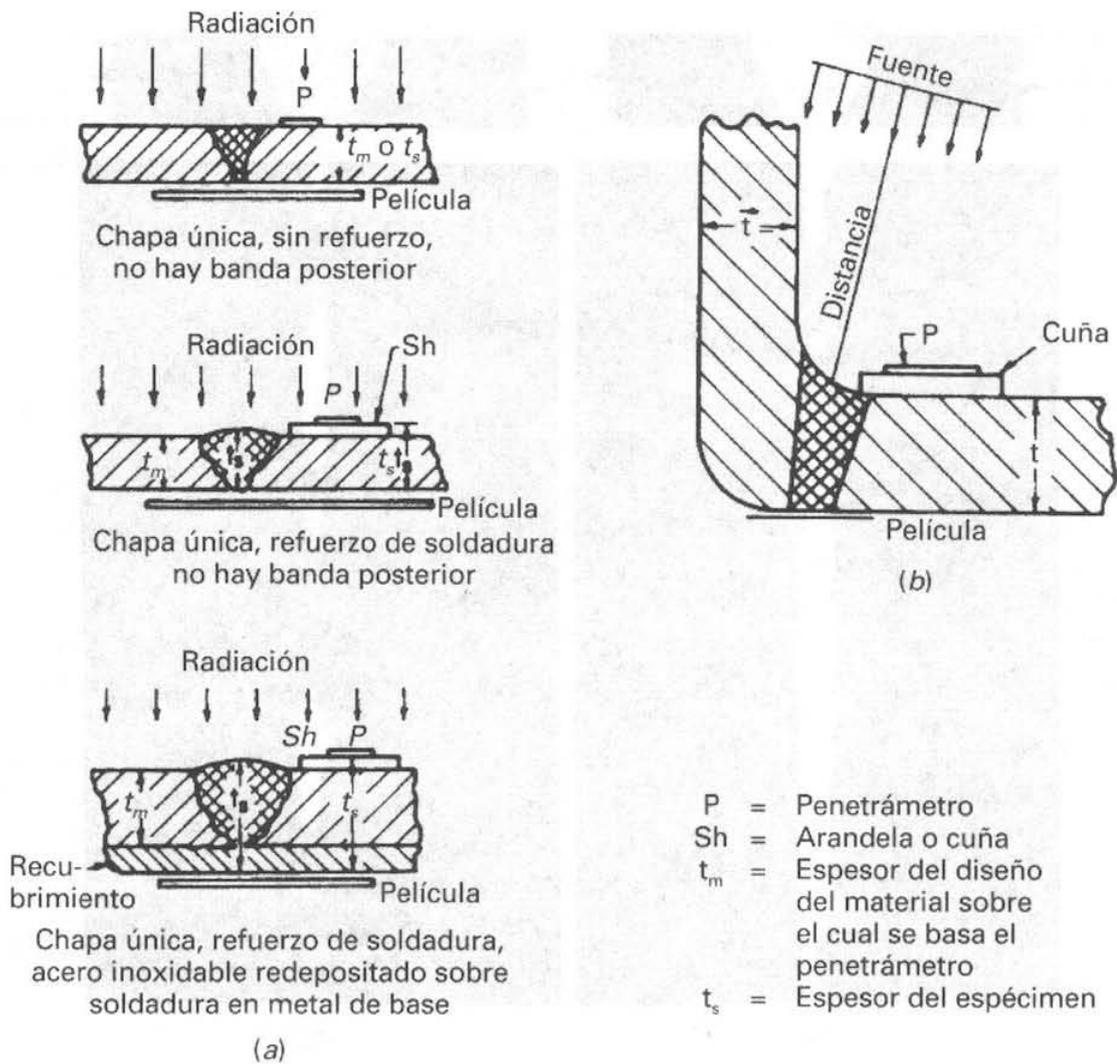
Penetrámetro y situación de la arandela o cuña en radiografía. (a) Para soldaduras a tope. (b) Para soldaduras tubulares.
